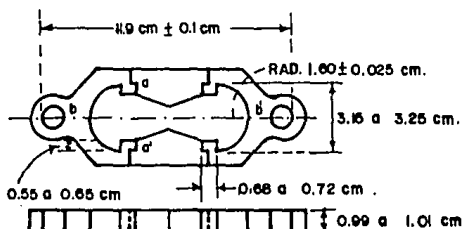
MOLDE DE PRUEBA DE DUCTILIDAD ASTM D115
